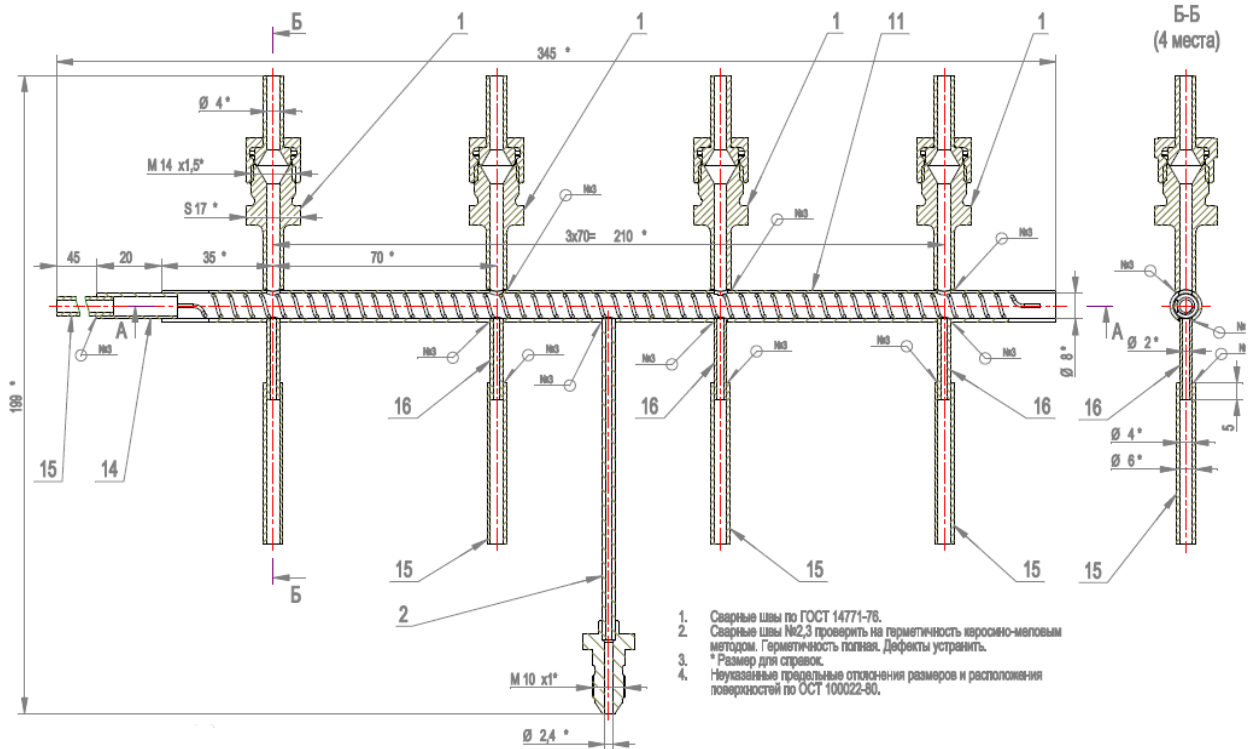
Фрагмент сборочного чертежа трубка со спиралью
